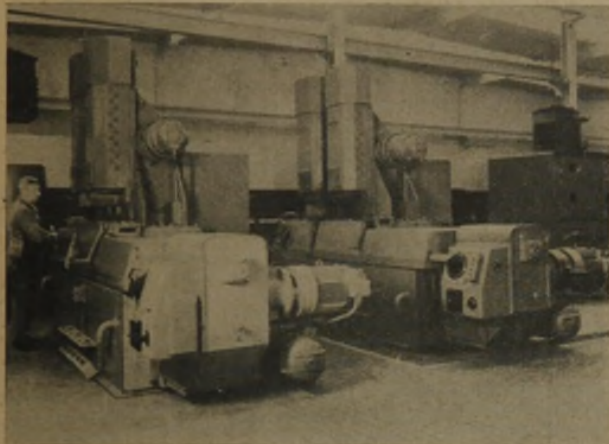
Zwei vollselbsttätige Abbrennschweißmaschinen je 160/320 KVA, für Querschnitte bis 12 000 mm²
